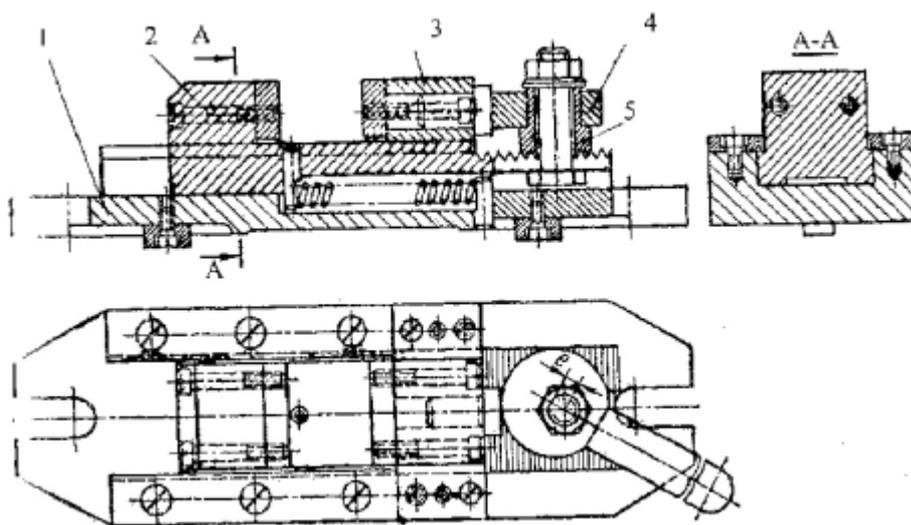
Конструкция эксцентриковых тисков: 1 – корпус; 2 – подвижная губка; 3 – неподвижная губка; 4 – эксцентрик; 5 – стойка.
